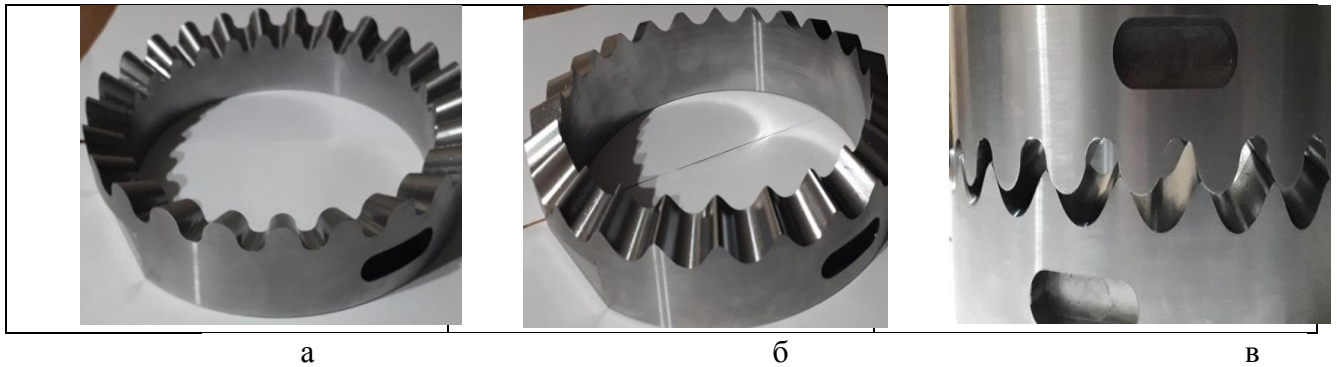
а) зубчатое колесо сателлита, б) центральное зубчатое колесо, в) колеса в зацеплении
